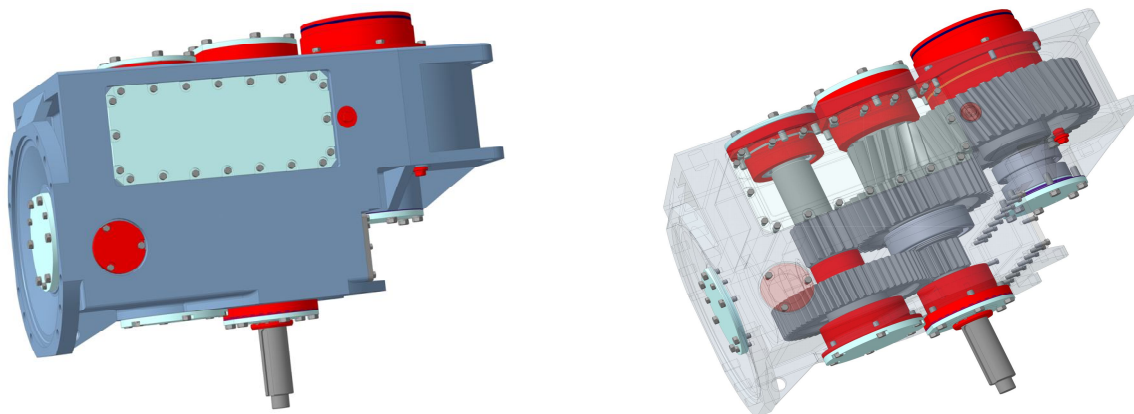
Твердотельная модель цилиндрического редуктора головной приводной станции
